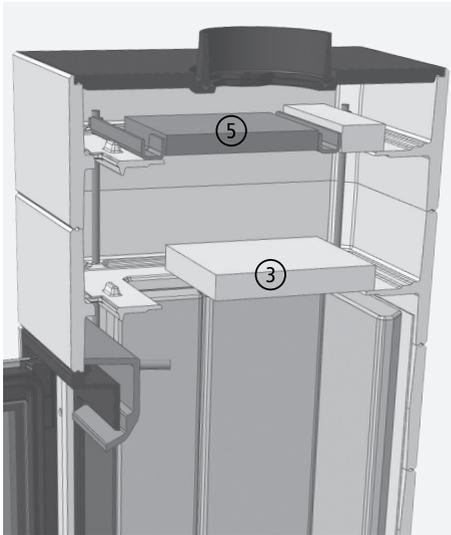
Position des plaques de catalyseur du CORNA tec, vue en coupe
